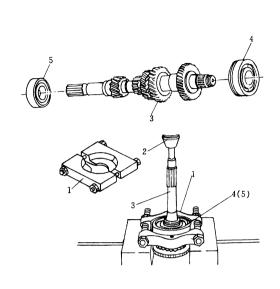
变速器第一轴的分解 1.工具 2.油压机 3.变速器第一轴 4、5.滚动轴承
